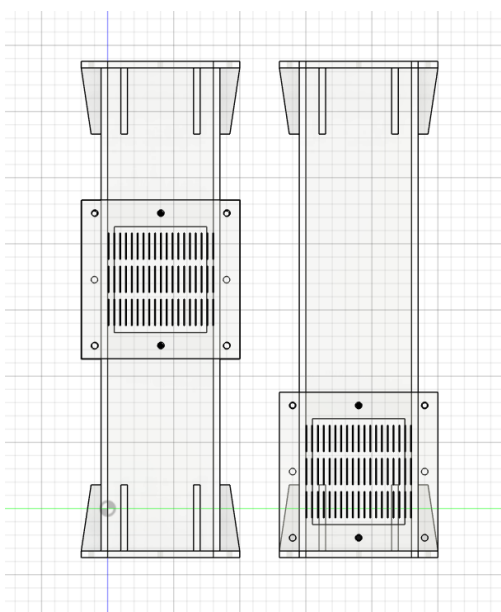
Modelo de torre com dreno lateral superior e dreno lateral inferior
